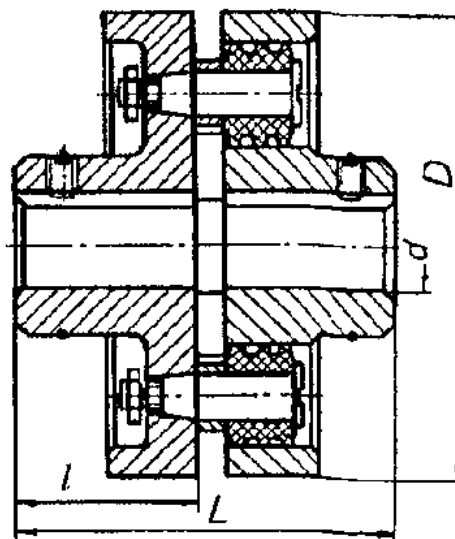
Упругая втулочно-пальцевая муфта: d – диаметр посадочного отверстия; D – наружный диаметр; L – длина муфты; l – длина полумуфты
